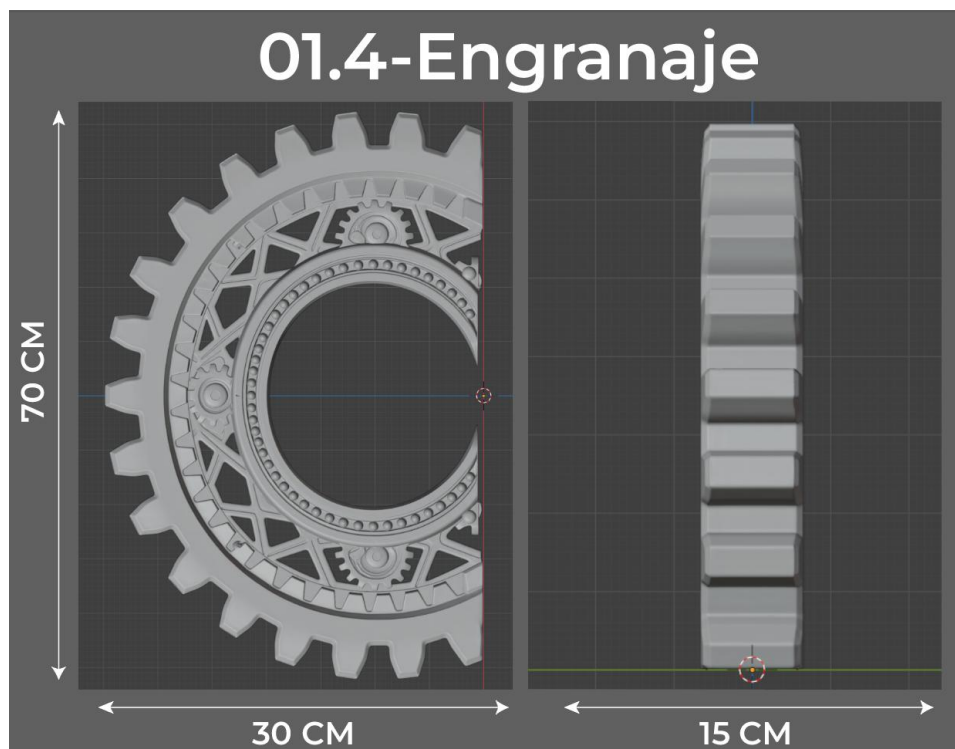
Modelado 3D y medidas de 01.4-Engranaje
